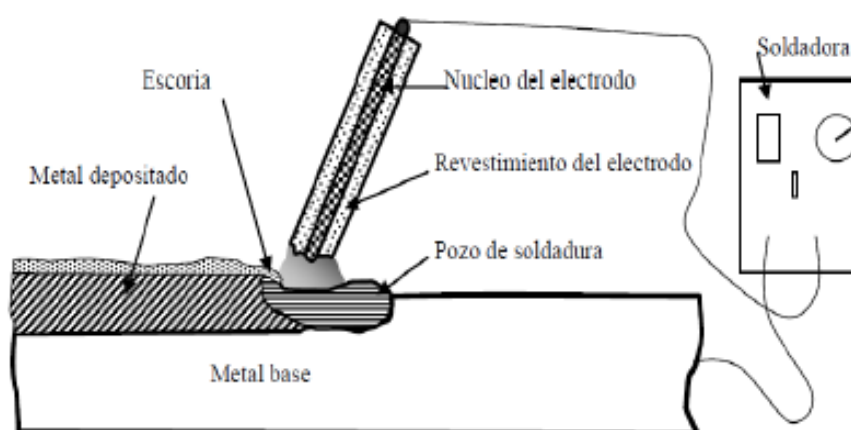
Componentes de la soldadura SMAW [28].
